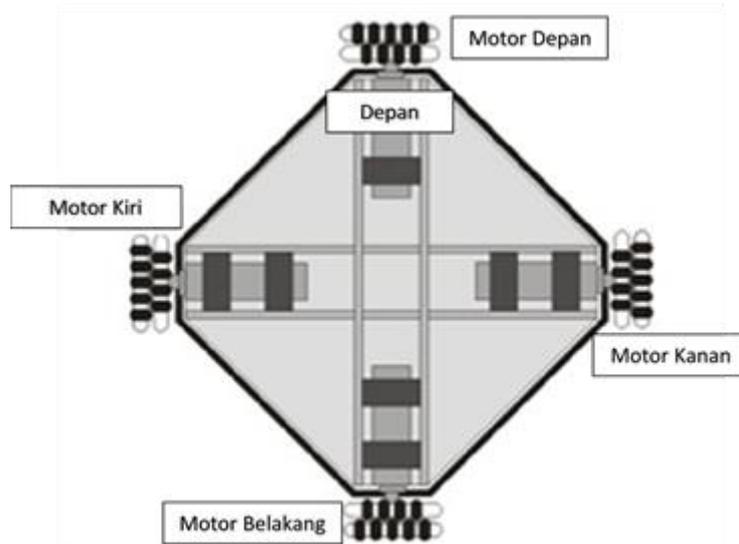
Sistem penggerak 4WD drive motor servo
